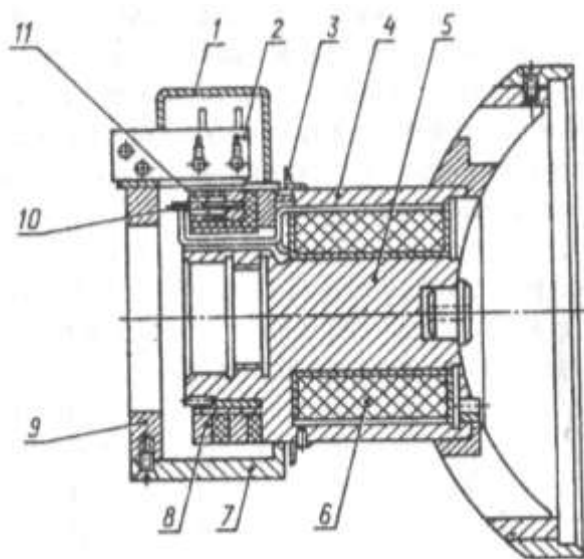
Круглый электромагнитный патрон для закрепления заготовок тонких плоских деталей
